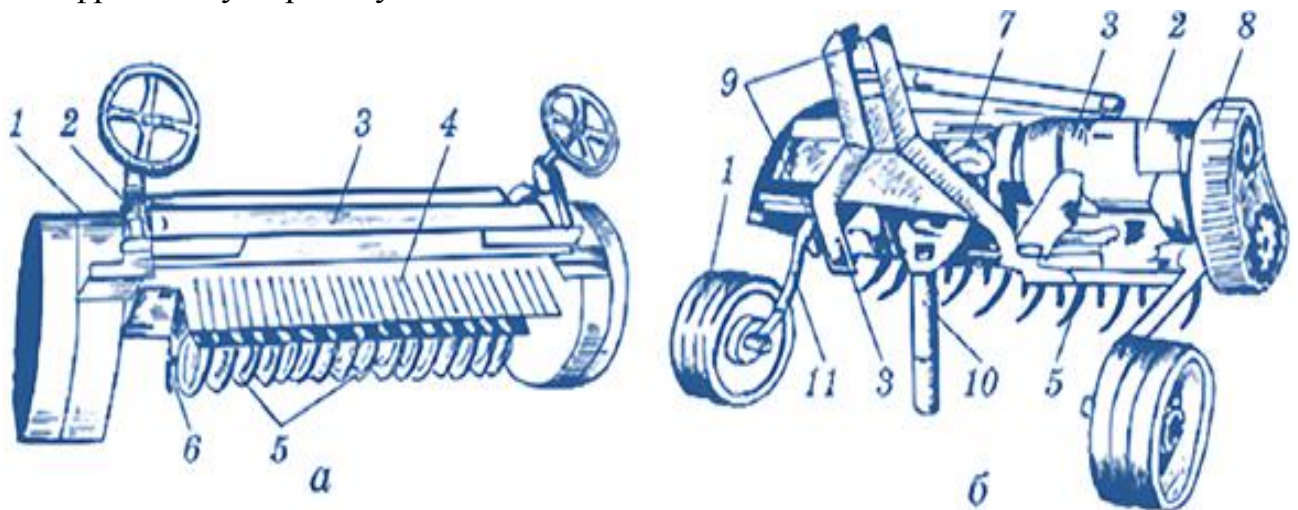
Ґрунтообробні фрези: а – причіпна (вигляд ззаду); б – начіпна (вигляд спереду); 1 – опорне колесо; 2 – гвинтовий механізм регулювання глибини фрезерування; 3 – кожух; 4 – граблі; 5 – ножі; 6 – сошник; 7 – редуктор; 8 – бортовий редуктор; 9 – місця кріплення до важелів і тяги начіпної системи; 10 – карданно- телескопічний вал; 11 – колінчаста піввісь
